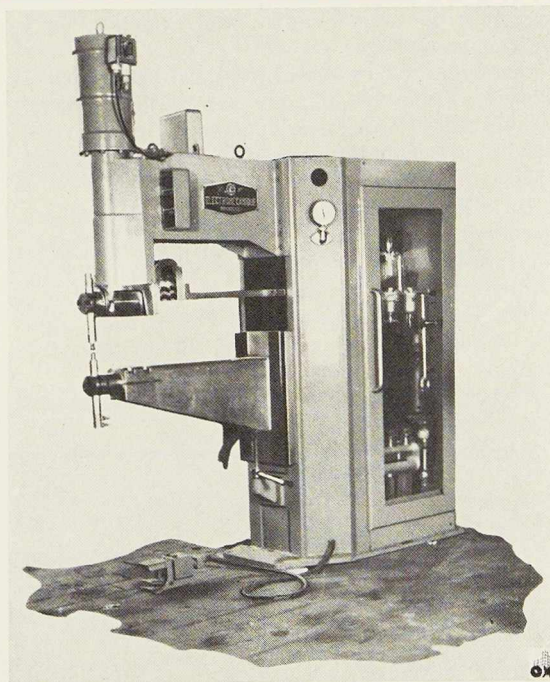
(ci-dessus). Machine à souder par point - type SEPAL 250.
